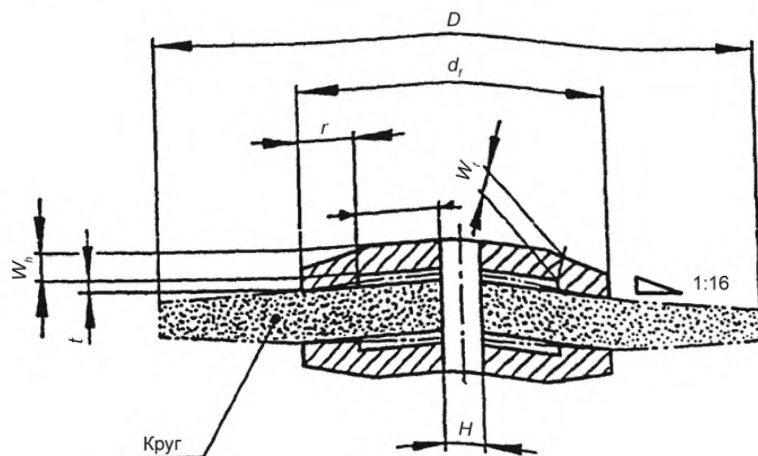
Фланец для шлифовальных кругов с двухсторонним коническим профилем типа 4
